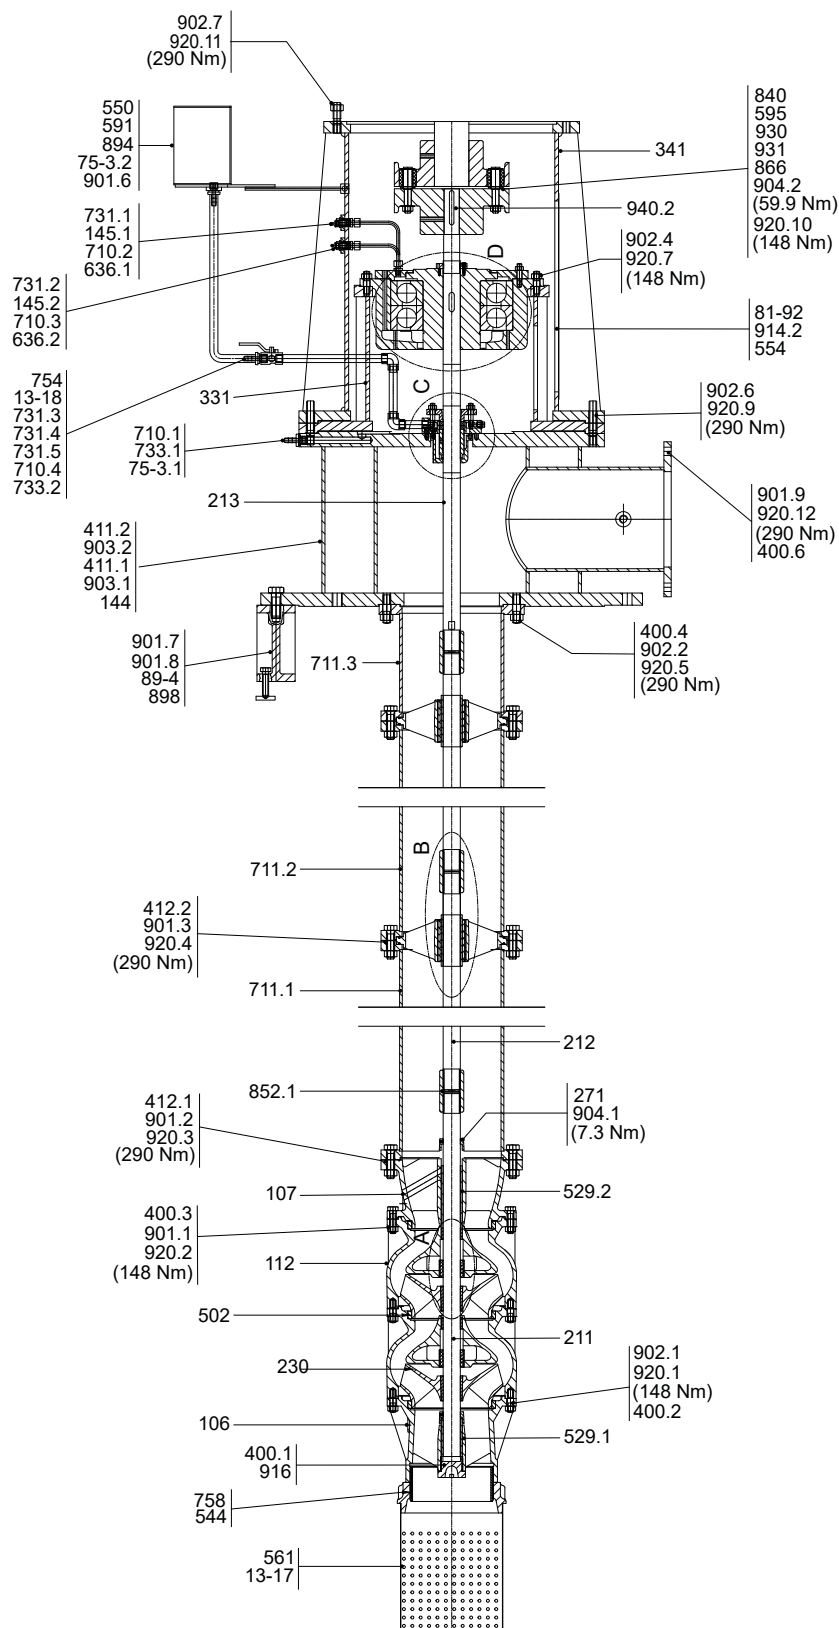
Schnittzeichnung mit Einzelteileverzeichnis
